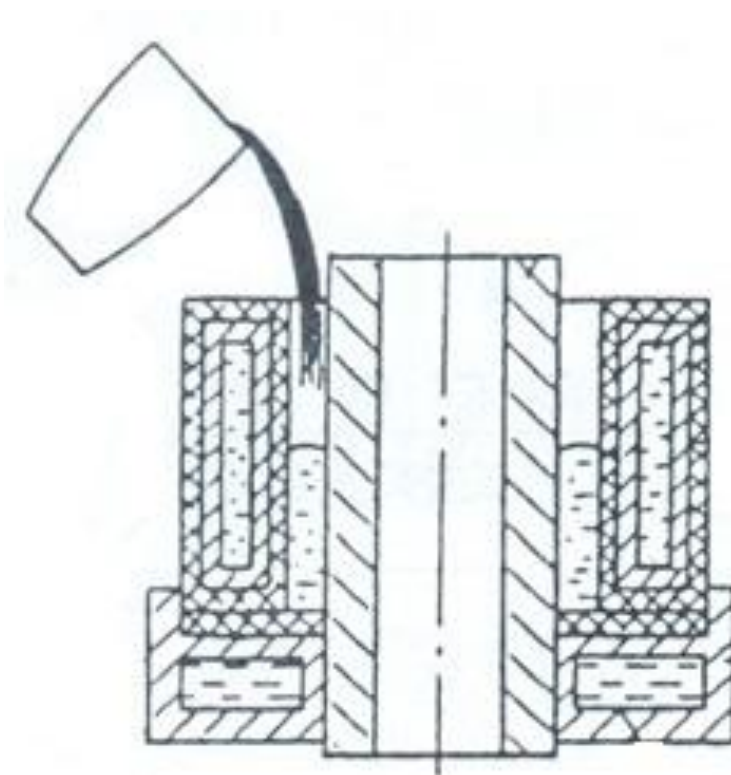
Индукционная наплавка заливкой жидкого присадочного металла на подогретый основной металл
